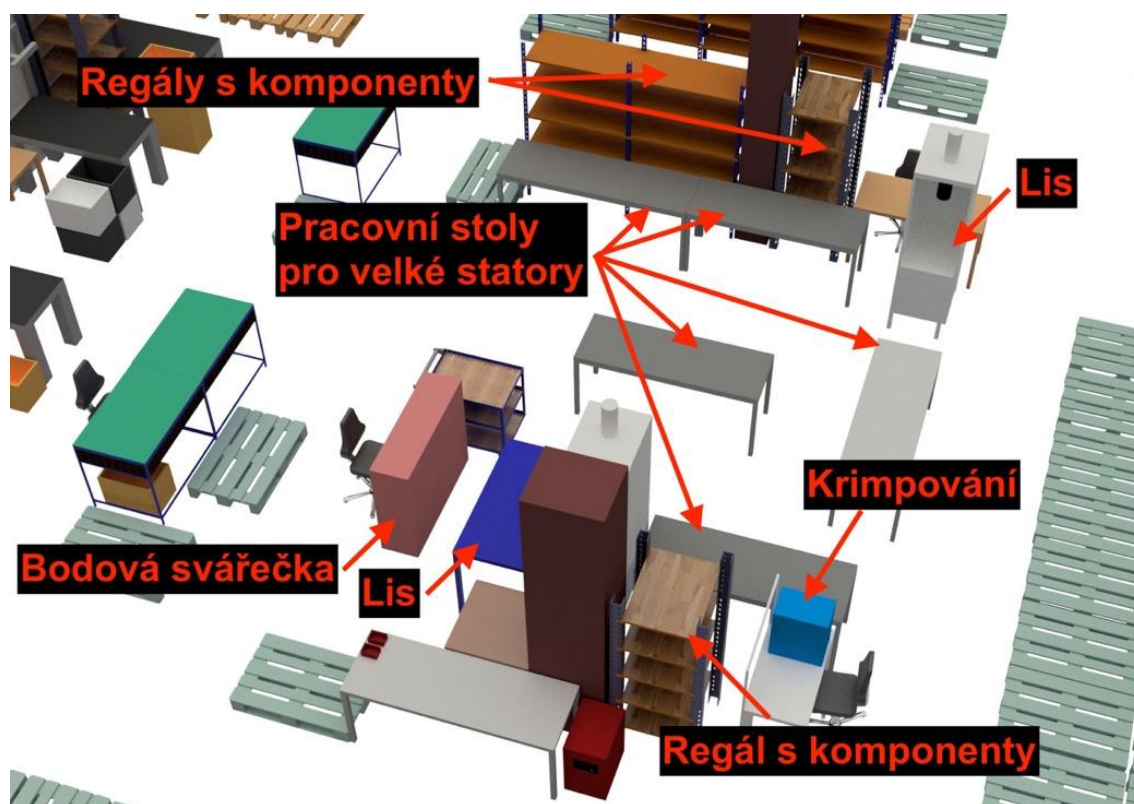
Detail s rozpracovanou výrobou a vstupním materiálem
